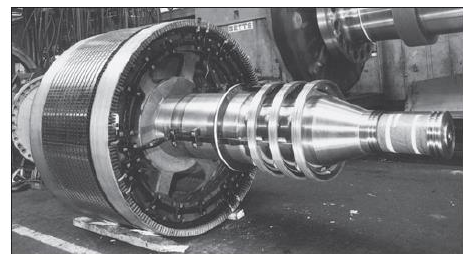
ESTRUTURA DO ROTOR BOBINADO. FONTE: (STEPHEN, 2013).
